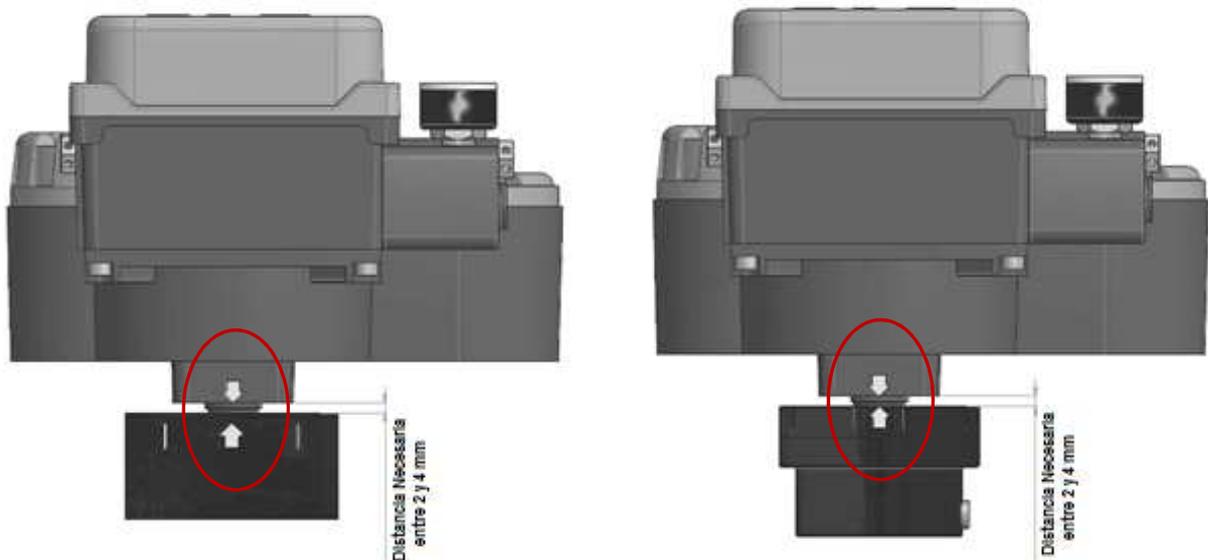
Montaje del VVP10-H en imán lineal. Figura 2.8 – Montaje del VVP10-H en imán rotativo.
